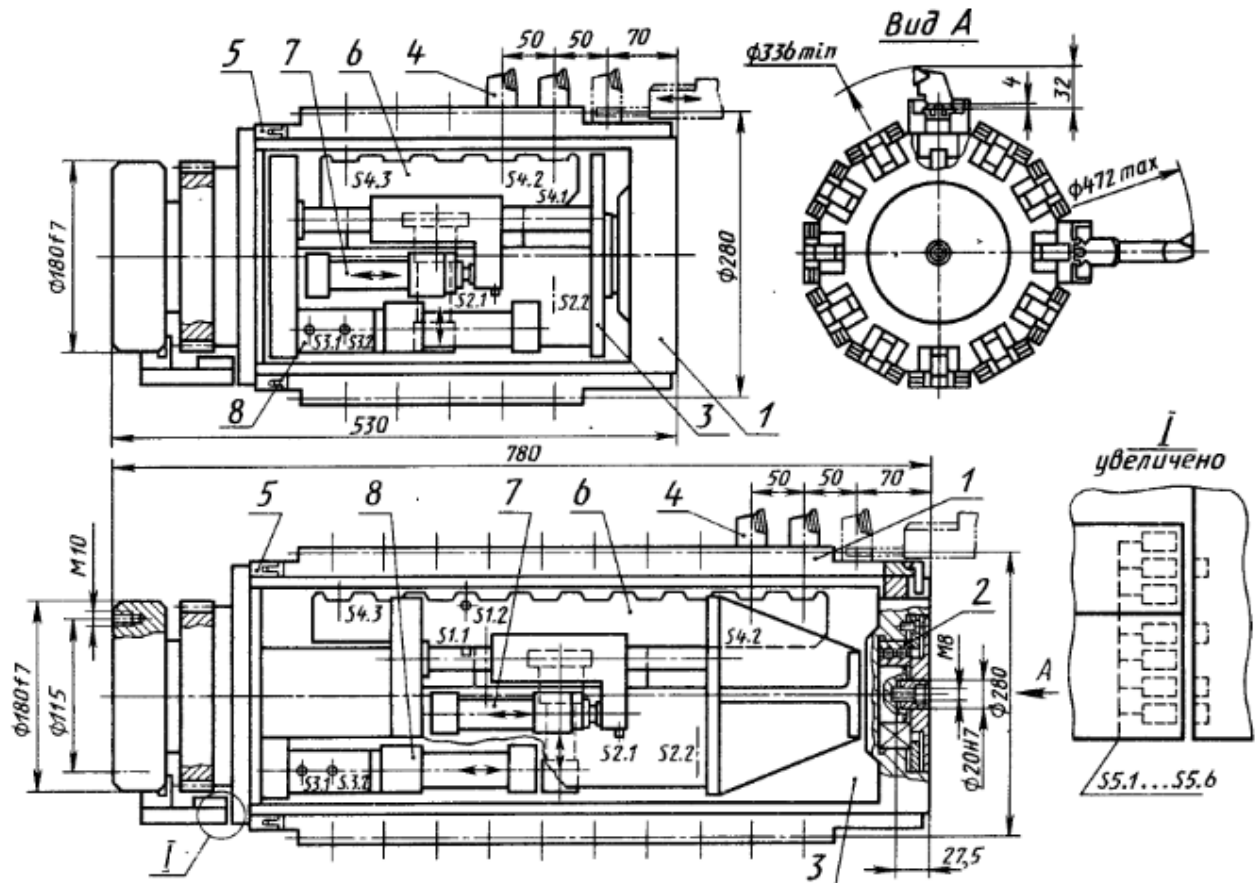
Загальний вигляд інструментального магазину з механізмом привода.
